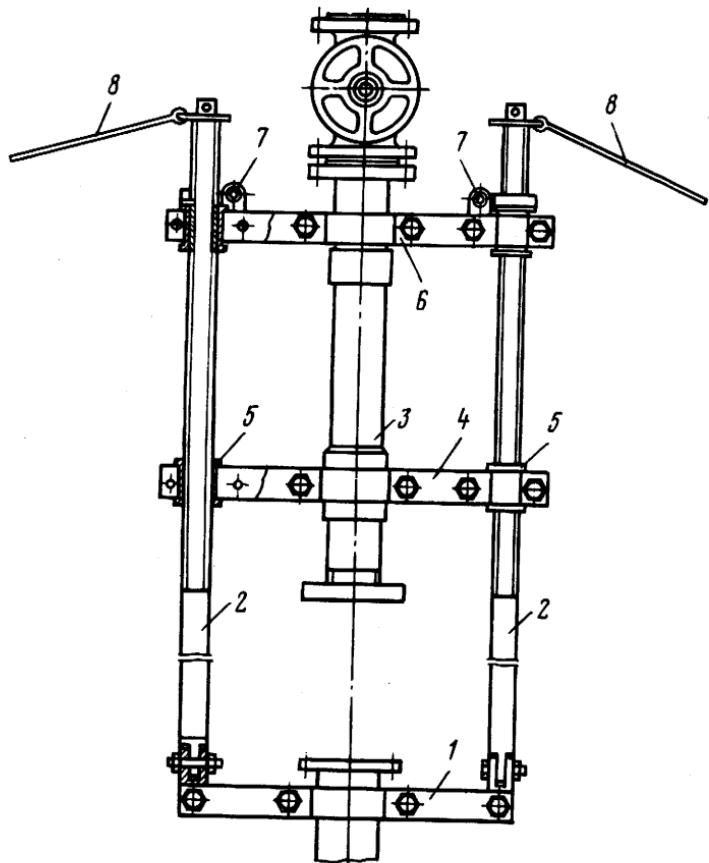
Приспособление для установки запорной арматуры (винтовой натаскиватель)
